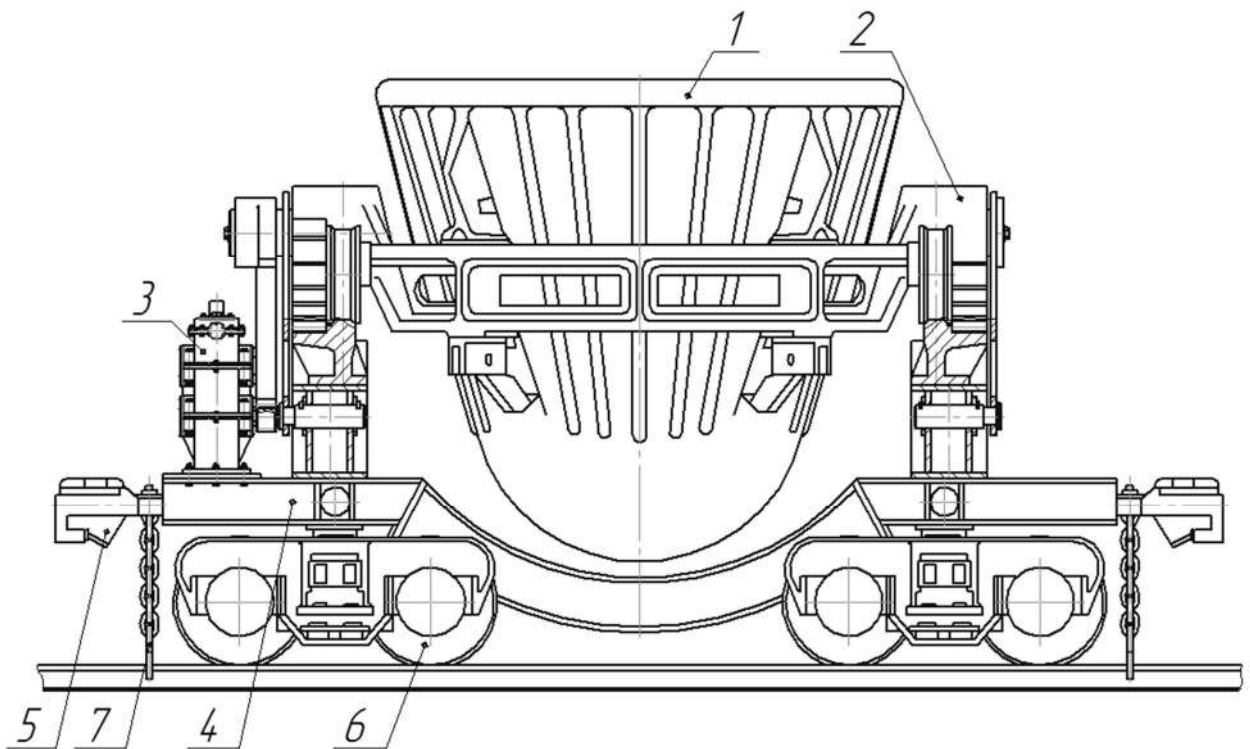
Загальний вид існуючої конструкції шлаковоза ШТД-16,5
